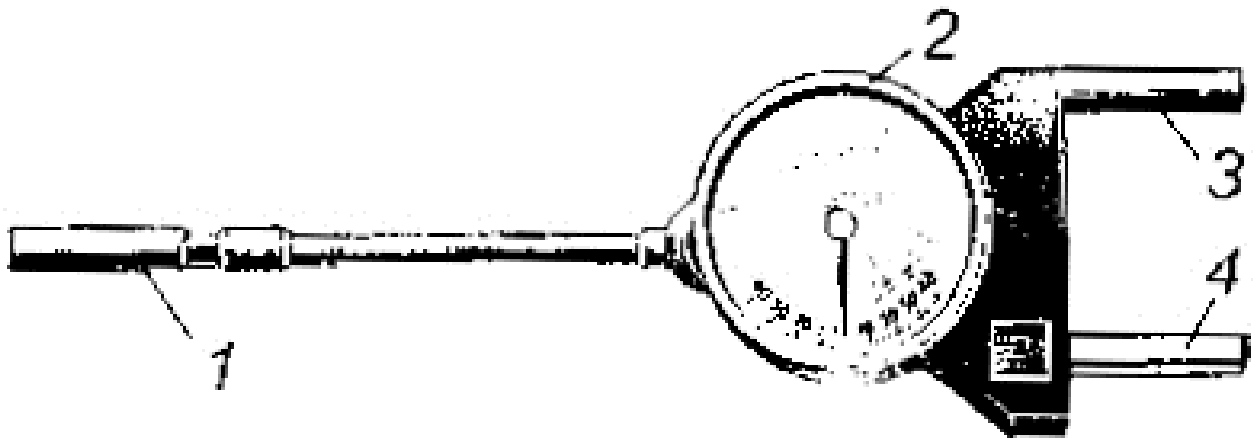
Прилад К - 428 для визначення кутового зазору трансмісії: 1 - рукоятка; 2 - динамометричний пристрій; 3 - нерухома губка; 4 - рухлива губка
